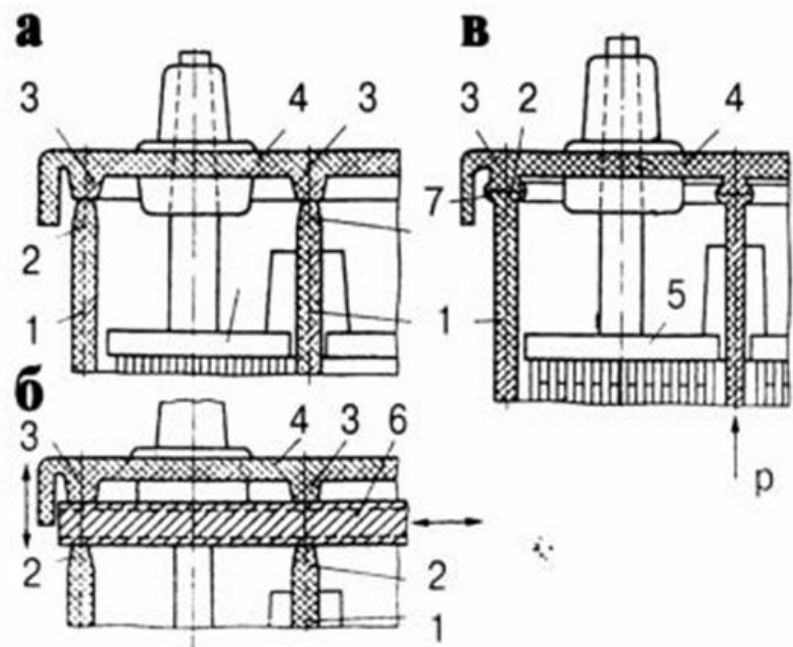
Соединение общей крышки с моноблоком методом контактно-тепловой сварки:
